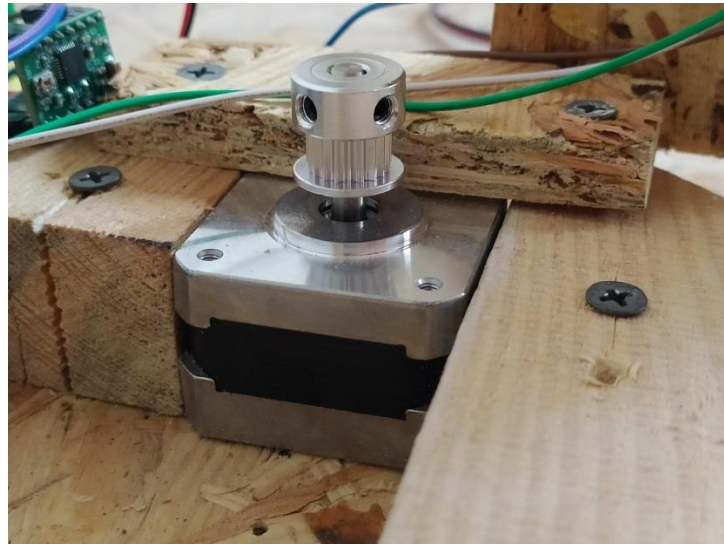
Загальний вигляд шківів поєднаного з валом двигуна
